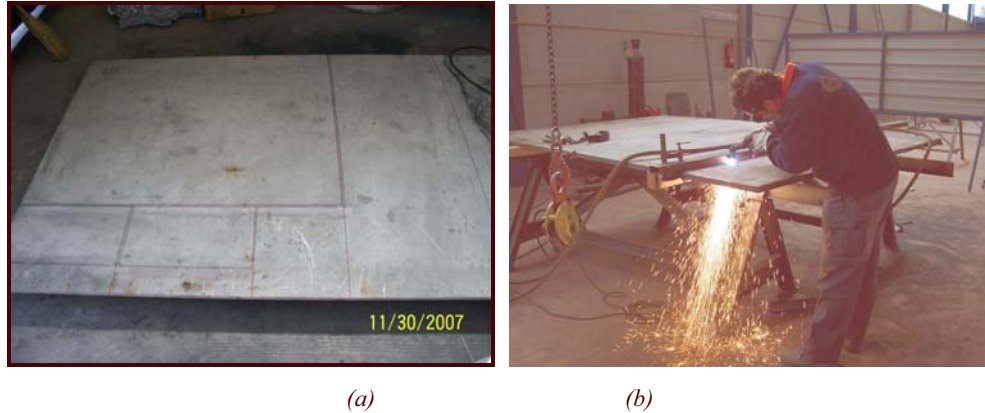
(a) Dimensionamiento de la placa de acero inoxidable AISI 304 y (b) corte de la placa con plasma en el IEE
